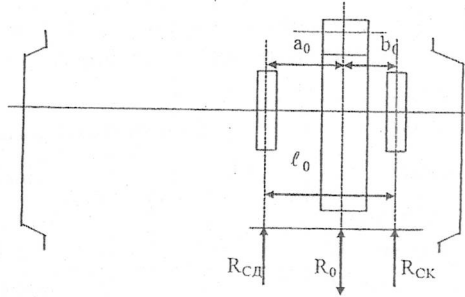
Схема для определения нагрузок на опорные подшипники тягового редуктора
